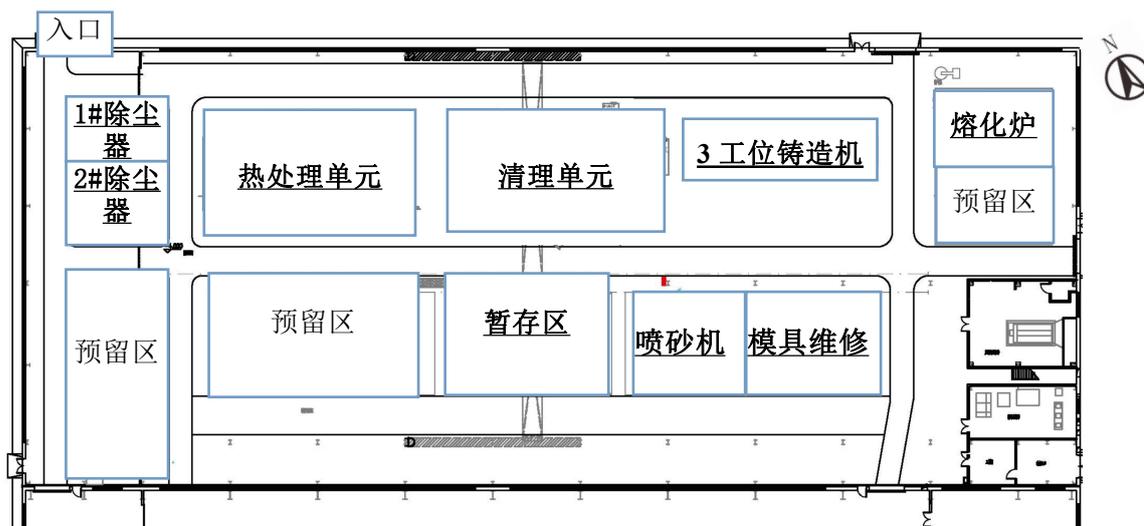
本项目内部平面布置（6-7 铸造车间北）
